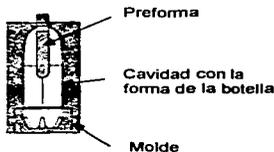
Introducción de la Preforma en la cavidad del molde.
